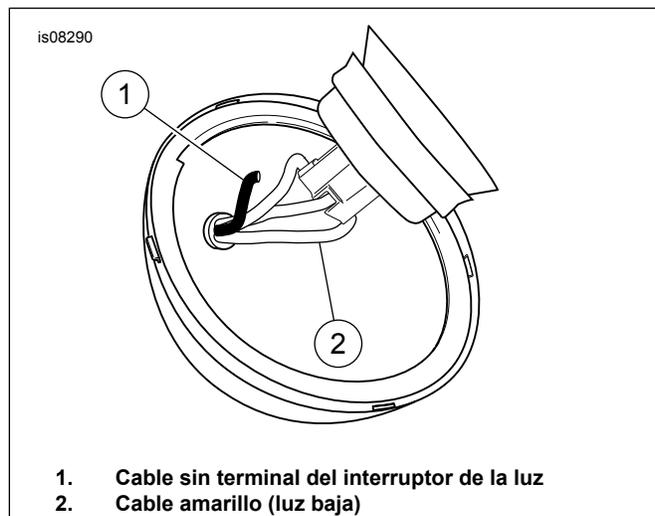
Empalme del cable sin terminar del interruptor con el cable amarillo (luz baja) del faro delantero
